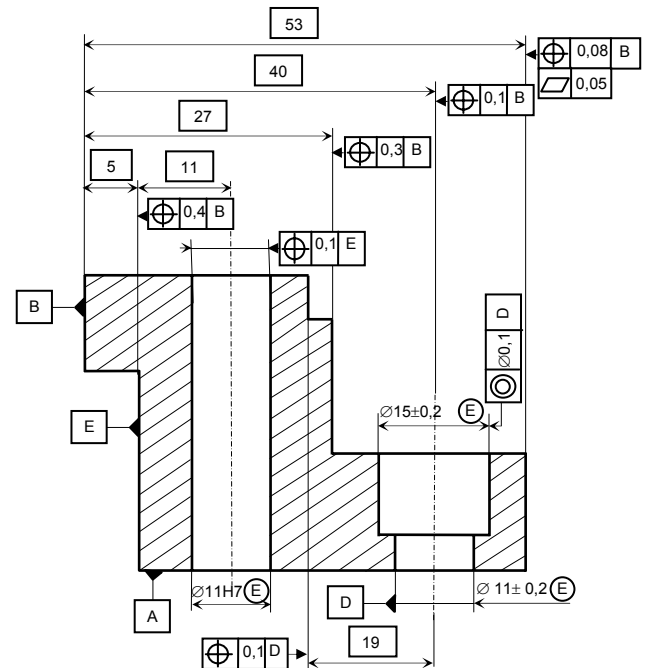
Dessin de définition de la pièce de fraisage (une vue)
